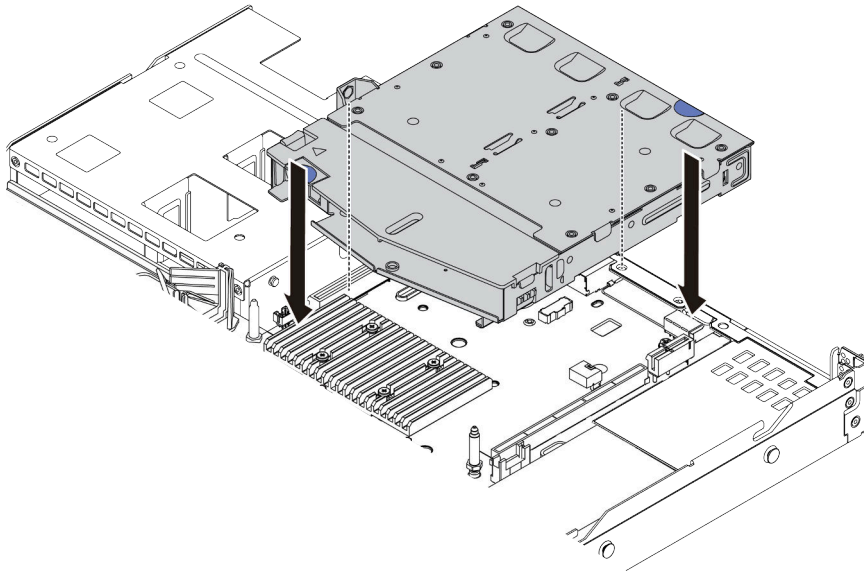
Installation der hinteren Hot-Swap-Laufwerkhalterung
